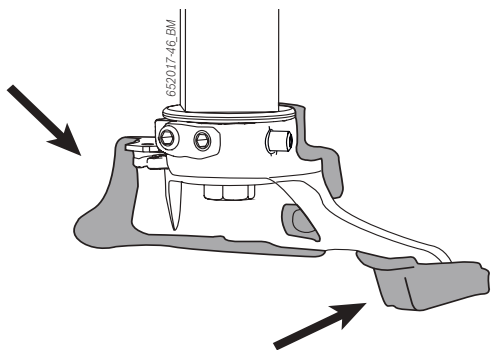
Instalación de los elementos protectores para el cabezal de montaje
